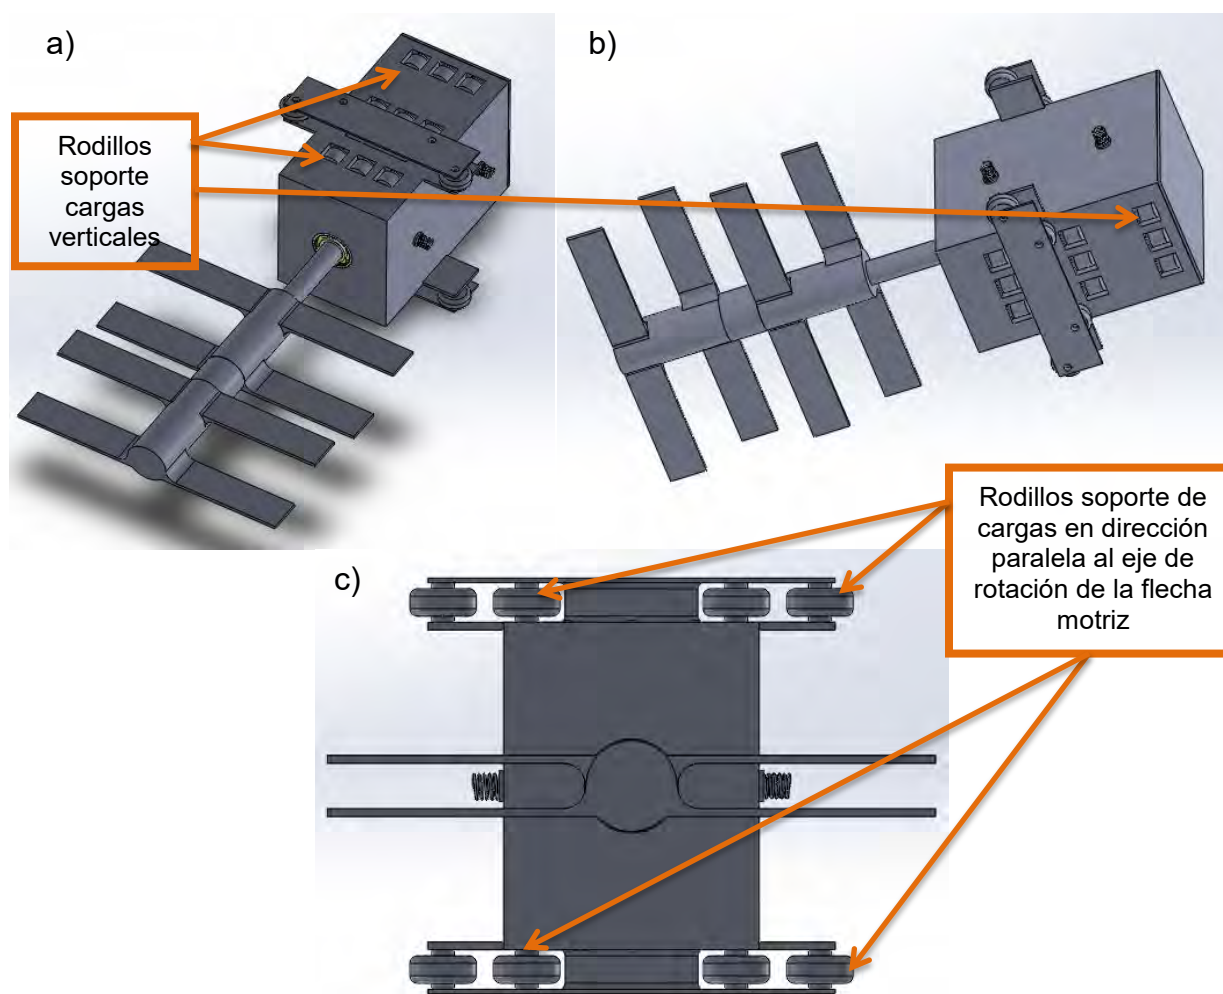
Modificación del conjunto motor, a) Vista 3D de la parte superior b) Vista 3D de la parte inferior, c) Vista frontal del conjunto motor
